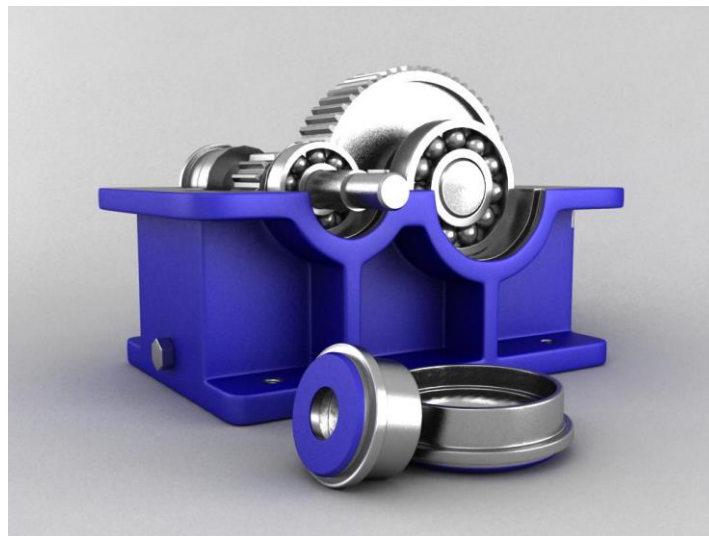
3D-модель цилиндрического одноступенчатого редуктора
